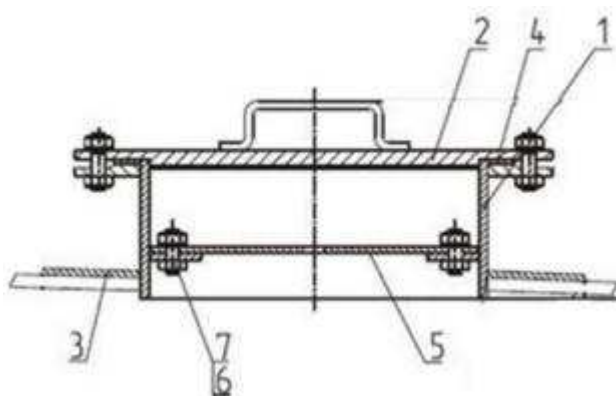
Общий вид светового люка: 1 – корпус, 2 – крышка, 3 – фланец усиливающий, 4 – прокладка, 5 – перемычка, 6 – болт, 7 – гайка
